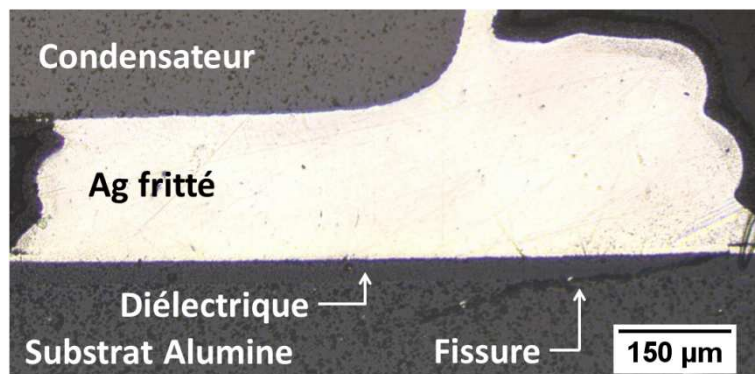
71 : Vue en micro-section de la fissuration du substrat en alumine
